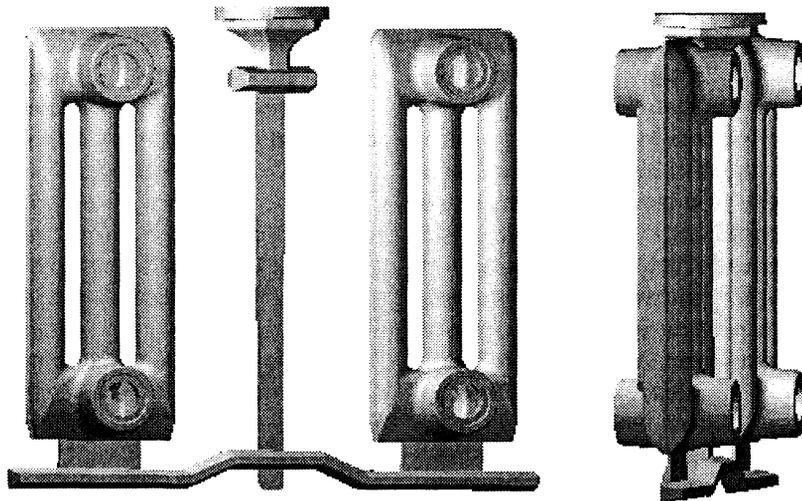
Твердотельные 3d-модели отливки «Радиатор БЗ-140x300»
